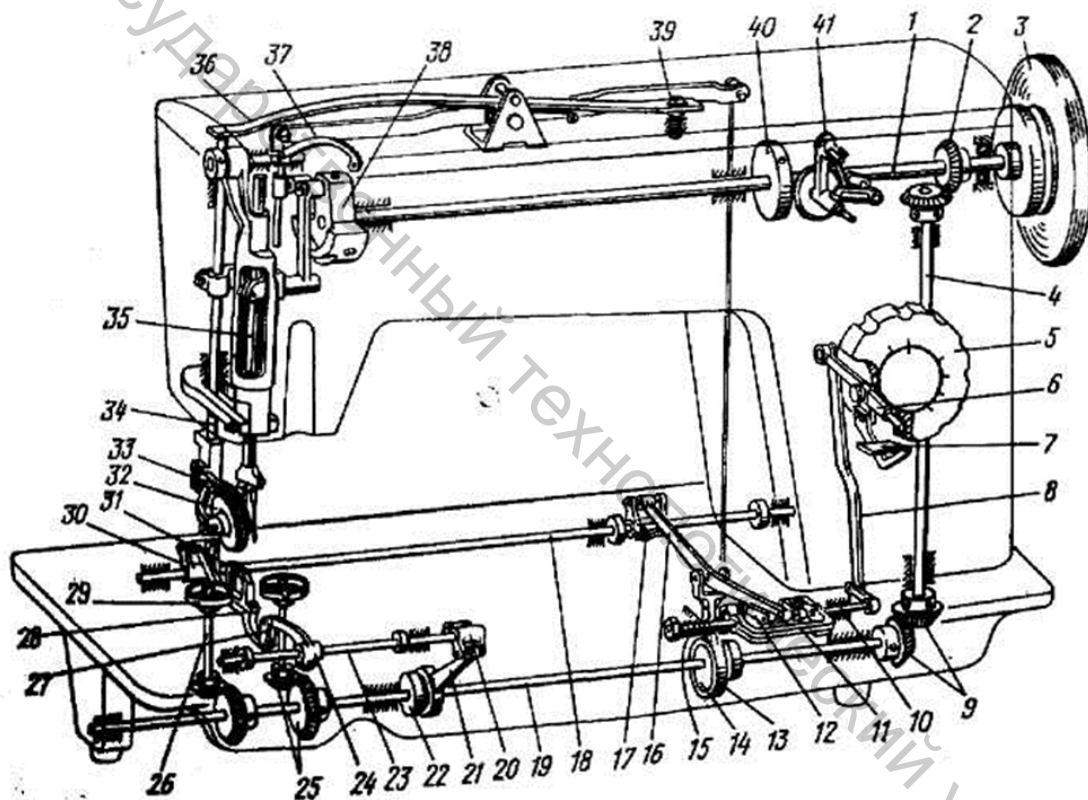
Схема двухигольной челночной швейной машины с плоской платформой
